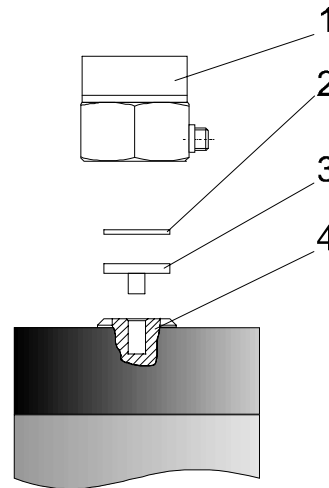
Крепление поверяемого ВИП с плоской опорной поверхностью
